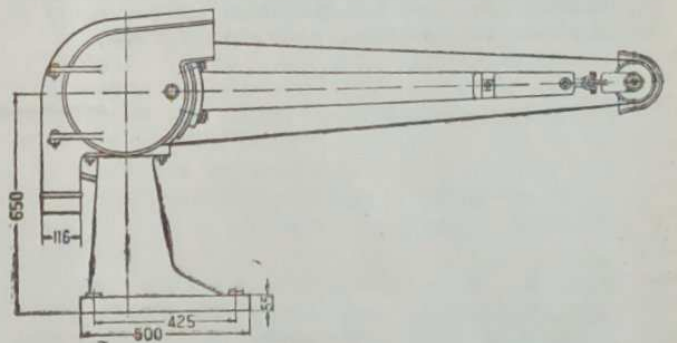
Шлифовально-ленточный станок со свободной лентой
